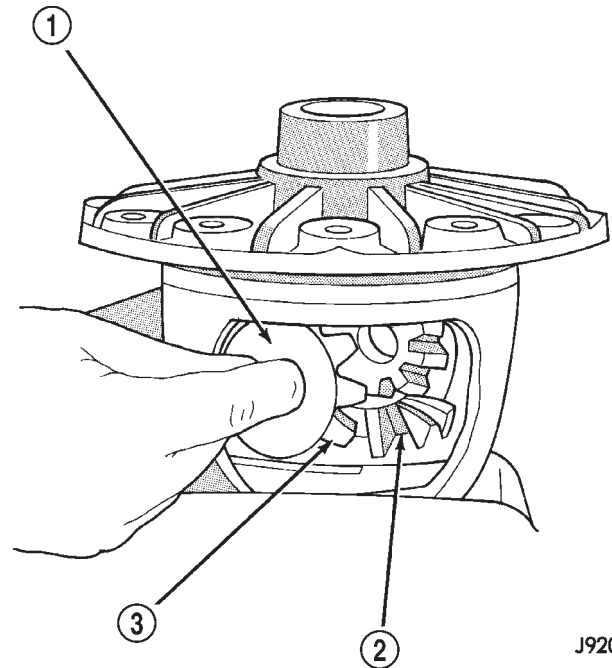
ENGRANAJE DEL DIFERENCIAL
